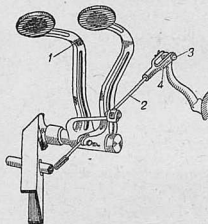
Привод механизма сцепления автомобиля ГАЗ М-1
